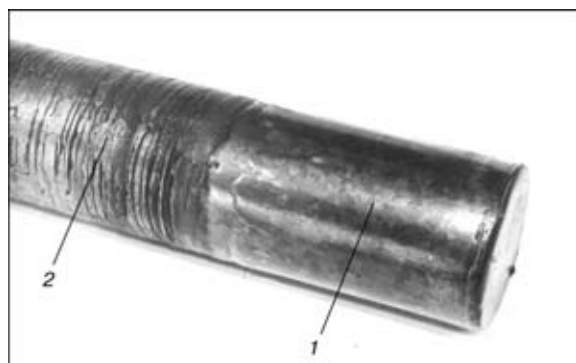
Внешний вид слитка циркония с оплавленной (1) и неоплавленной (2) боковой поверхностью
